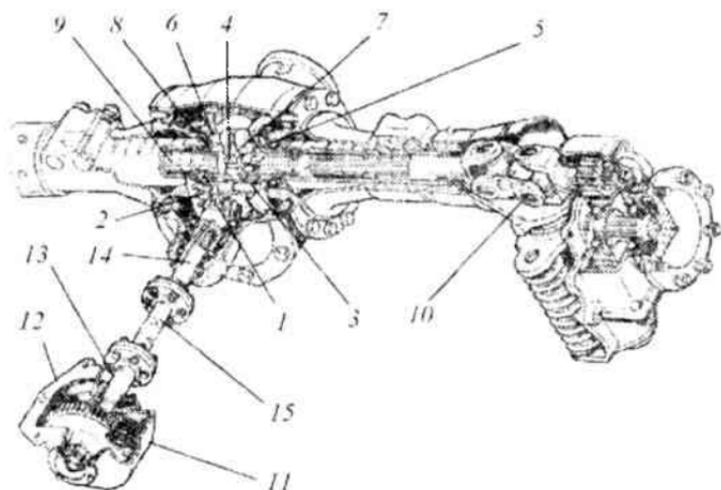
Передний мост трактора ЛТЗ - 82: 1 – шестерня; 2 – вал раздаточной коробки; 3 – ведущий вал главной передачи; 4 – ведомая шестерня; 5 – полуоси; 6 – тормозная шайба; 7 – ось; 8 – шлицевая обойма; 9 – собачка; 10 – крышка; 11 – сдвоенные карданы; 12 – корпус дифференциала; 13 – ведущая шестерня; 14 – вал привода; 15 – корпус раздаточной коробки;
